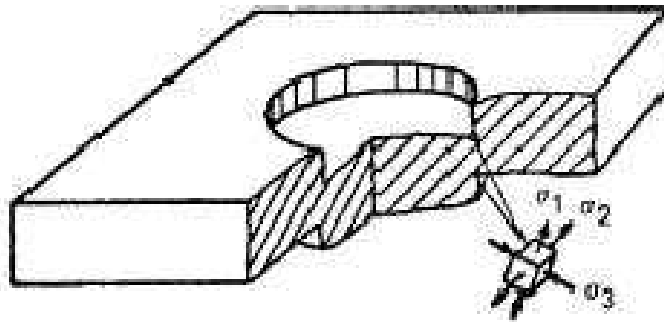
Напружений стан заготовки після чистового вирубання - пробивання.
